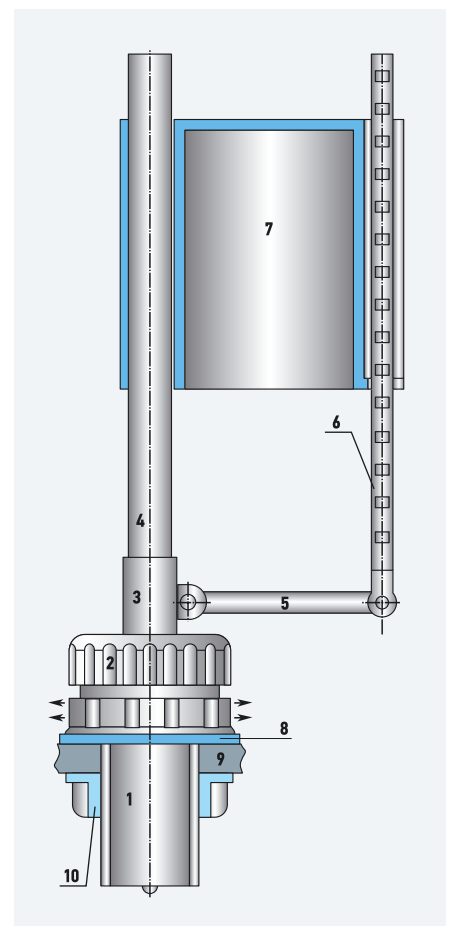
Конструктивная схема наполнительной арматуры с сервоуправлением с нижней подводкой (распределительная головка которой расположена на дне бачка) [1 — корпус наполнительной арматуры; 2 — накидная гайка; 3 — втулка; 4 — стойка; 5 — рычаг; 6 — тяга; 7 — поплавок; 8 — уплотнительная прокладка; 9 — дно смывного бачка; 10 — крепежная гайка]
